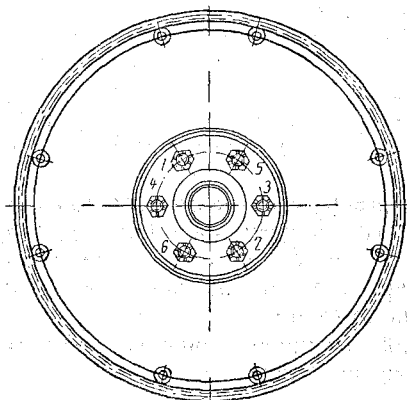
Порядок затягивания гаек крепления маховика к коленчатому валу
